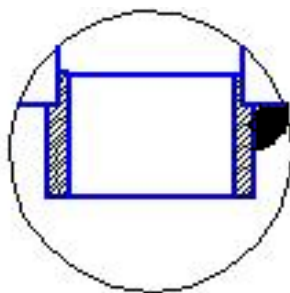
Сварное соединение Т1 по ГОСТ 14771-76
